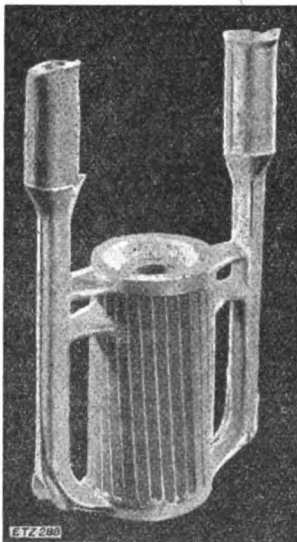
Im Kokillenguß hergestellter Käfigläufer mit Ausguß.
